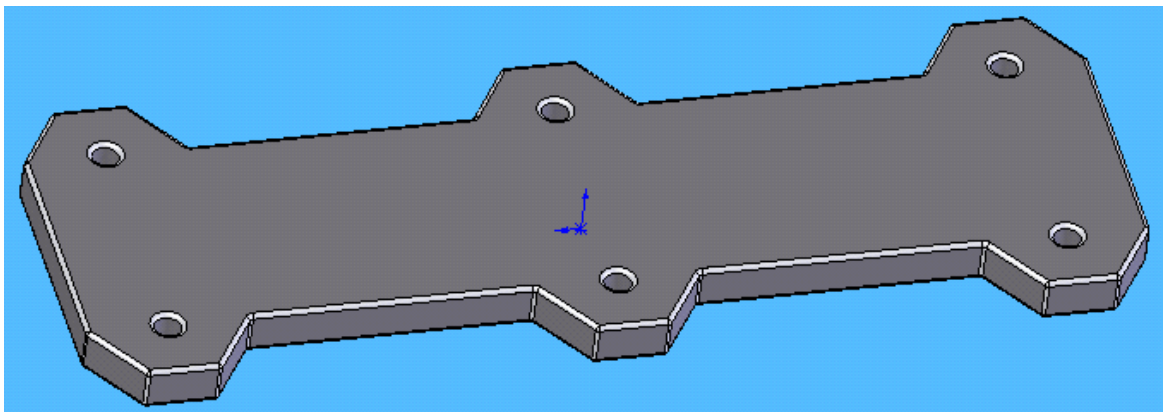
Placa principal con agujeros para acople de engranes y montaje de Hardware
